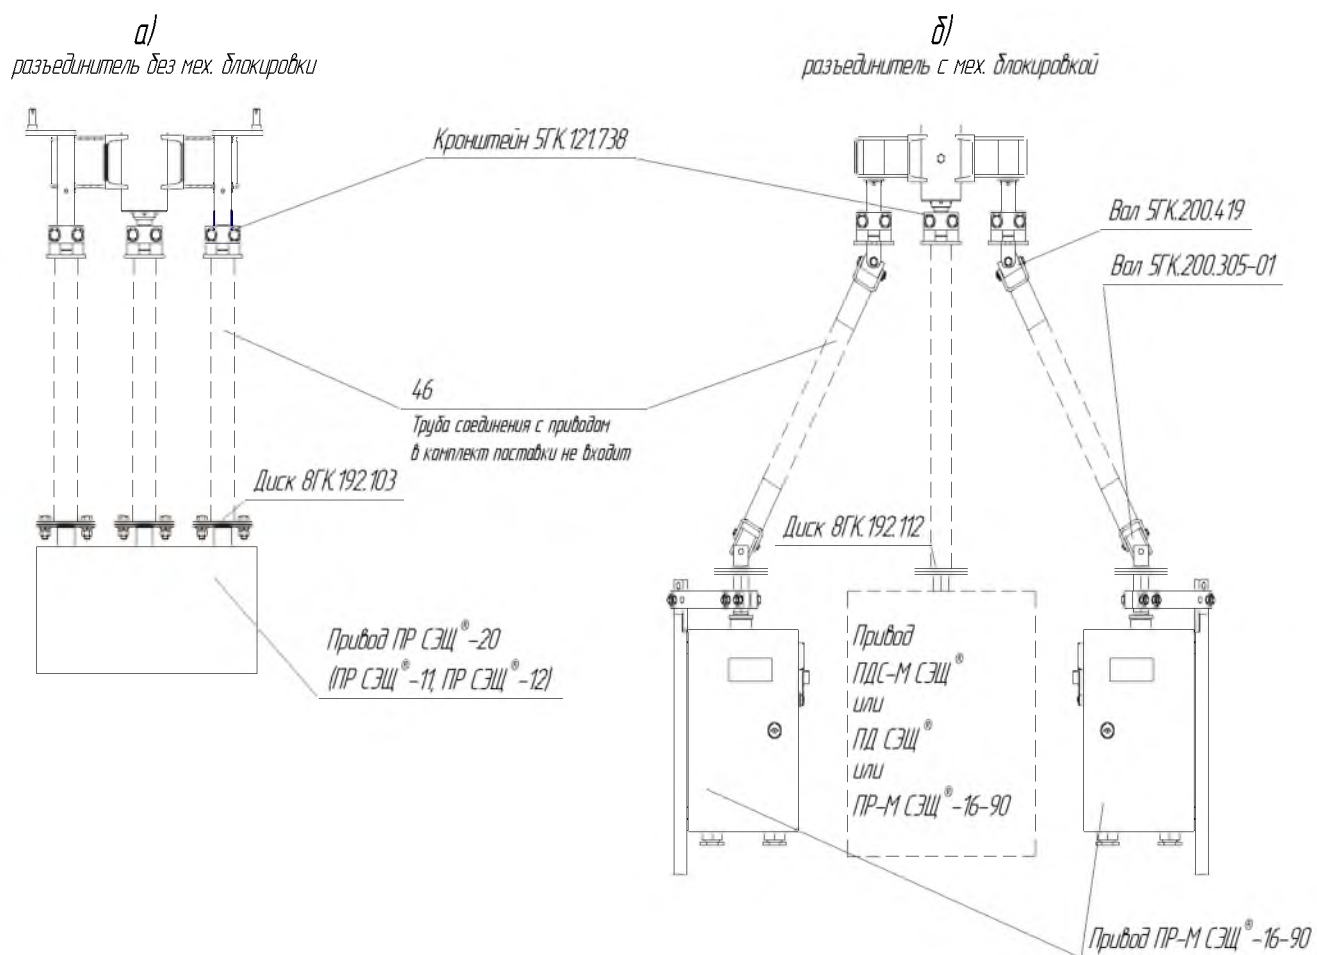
Схема установки приводов управления разъединителем
